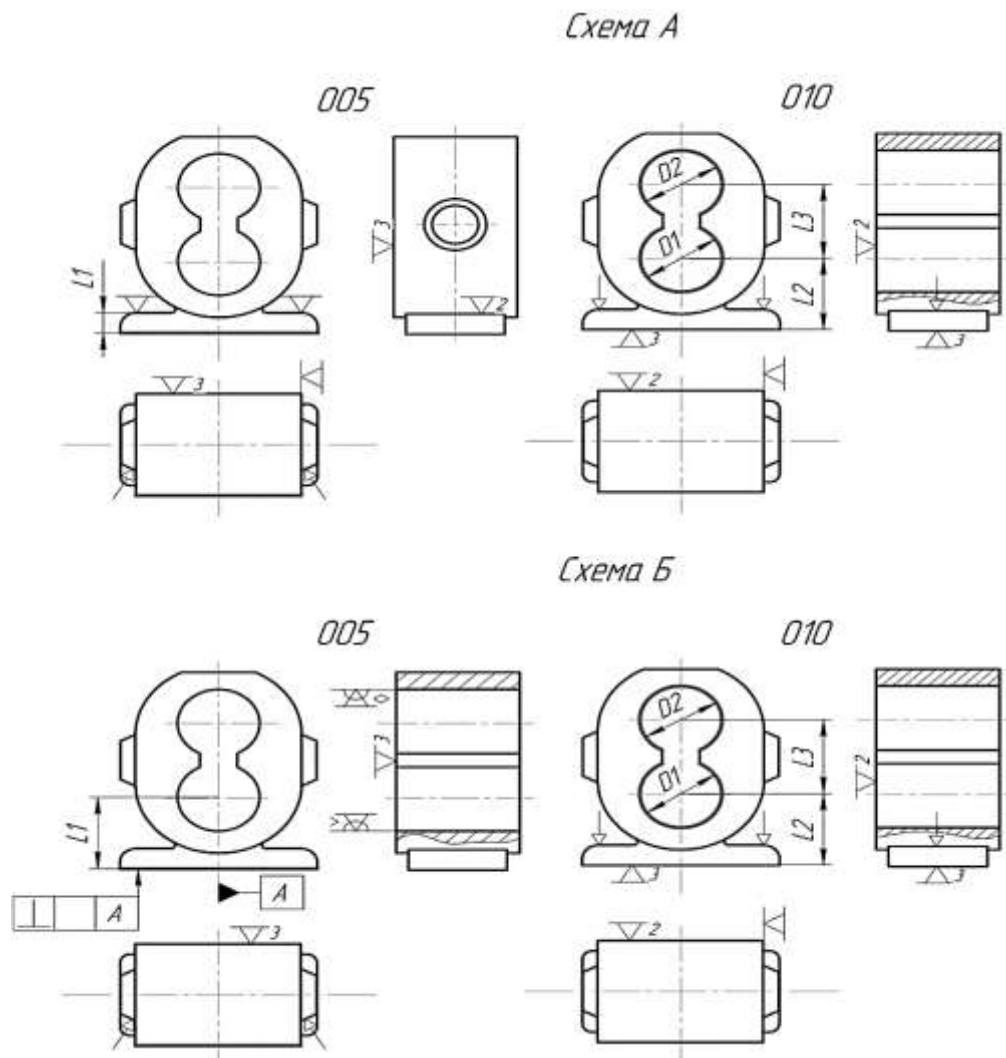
Схемы базирования литой заготовки (005 и 010 – номер операции)
